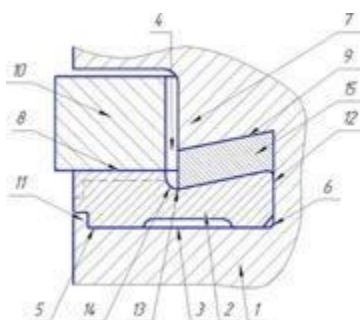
Схема установки противоизносного кольца с металлической проставкой: 1 – поршень; 2 – противоизносное кольцо; 3 – боковая поверхность кольца; 4 – поршневая канавка;
